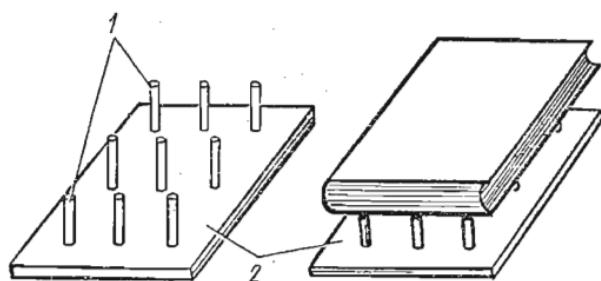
Подставка с шипами для двусторонней промазки форзаца:
